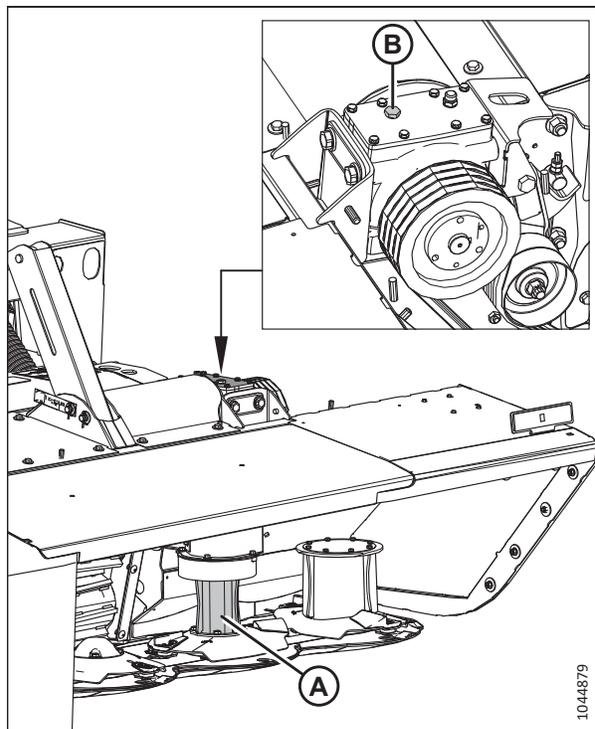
Côté gauche de la faucheuse à disques tractée
